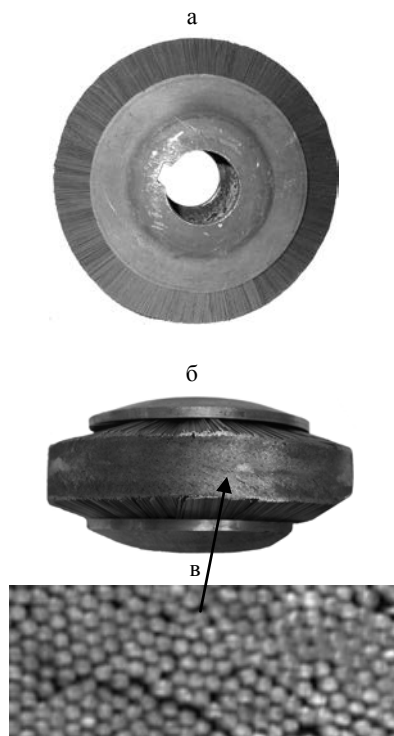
Иглофреза: а – внешний вид; б и в – рабочая поверхность иглофрезы (х20)
